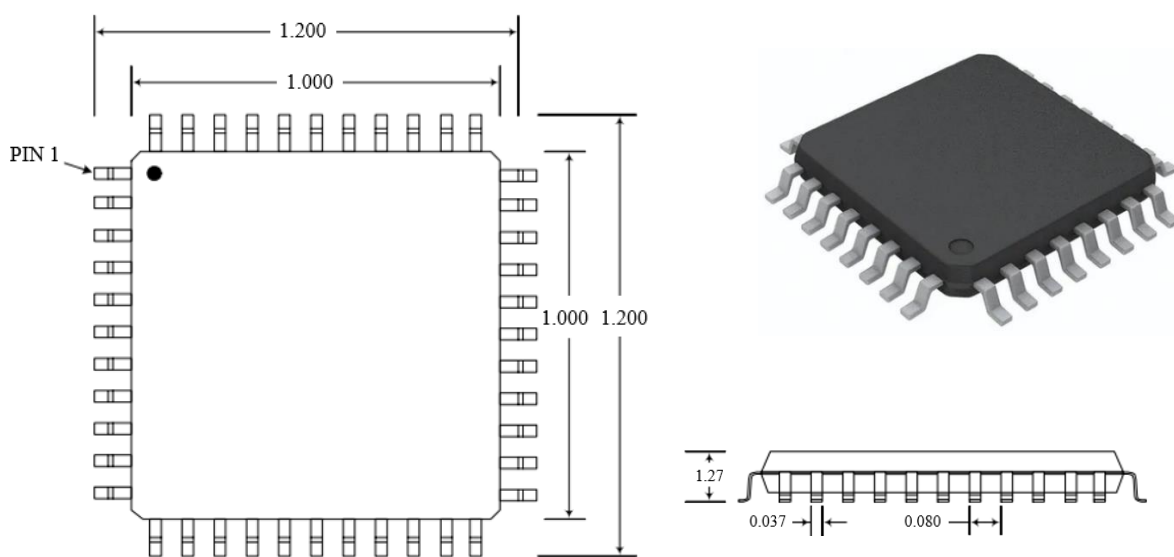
Пластиковый корпус QFP с 44 контактами.
